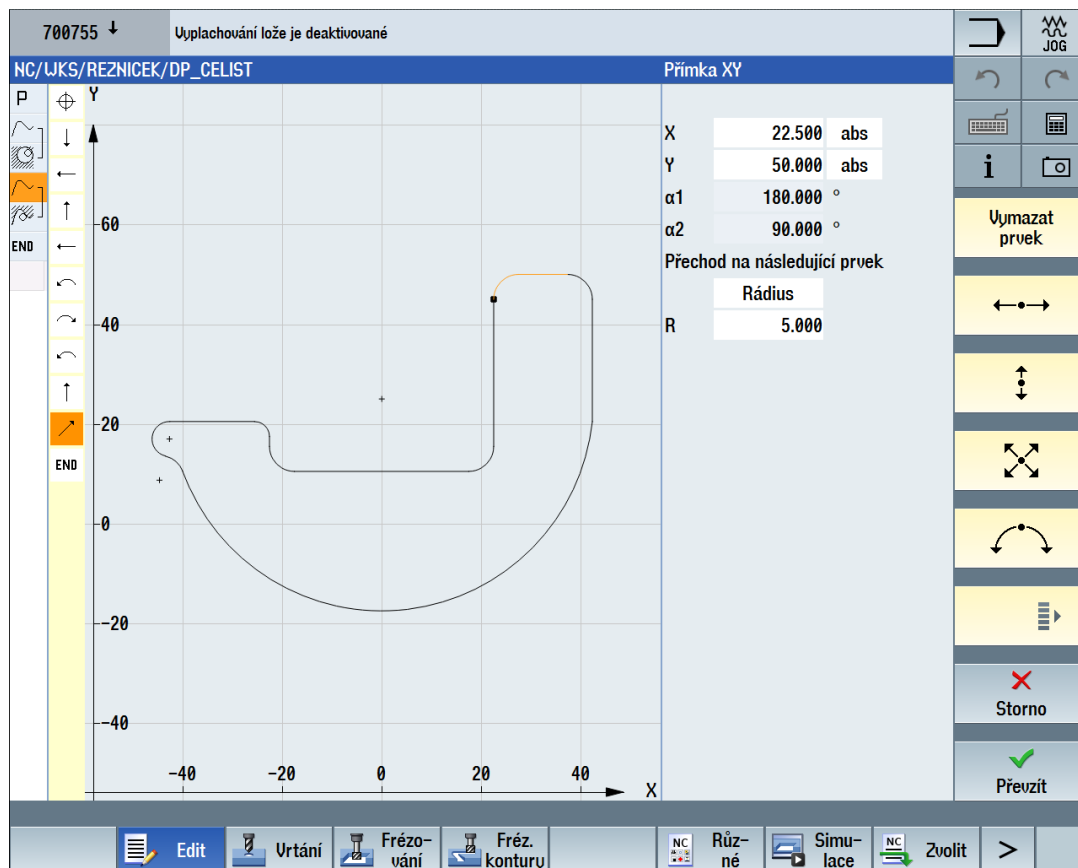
Kontura hrubování polotovaru testovacího přípravku
